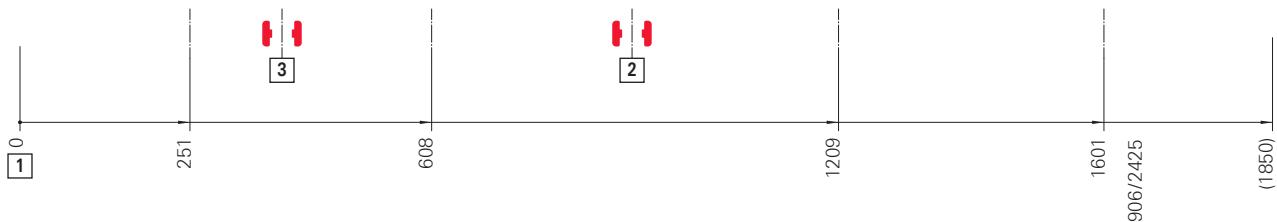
[1] tope perfil de deslizamiento; [2] posición de adaptador para bulón de cierre 1906; [3] posición de adaptador para bulón de cierre 2425
